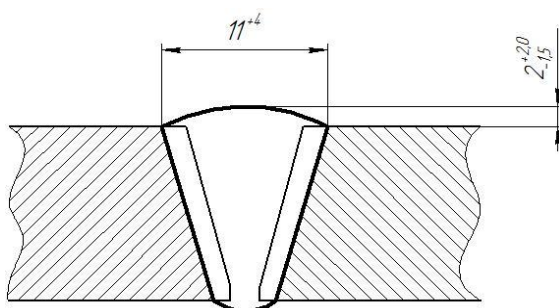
Размеры сварного шва при соединении труб диаметром 325 мм толщиной стенки 12 мм
